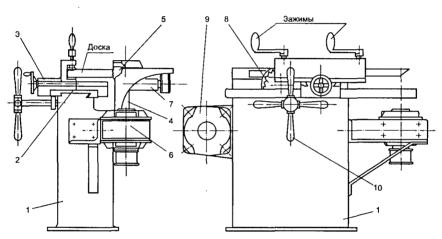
Общий вид станка для изготовления клиньев: 1 — литая станина, 2 — салазки горизонтального хода, 3 — салазки поперечного хода, 4 — вал фасонной фрезы, 5 — фасонная фреза, 6 и 9 — электродвигатель, 7 — вал дисковой пилы, 8 — дисковая пила, 10 — штурвал
